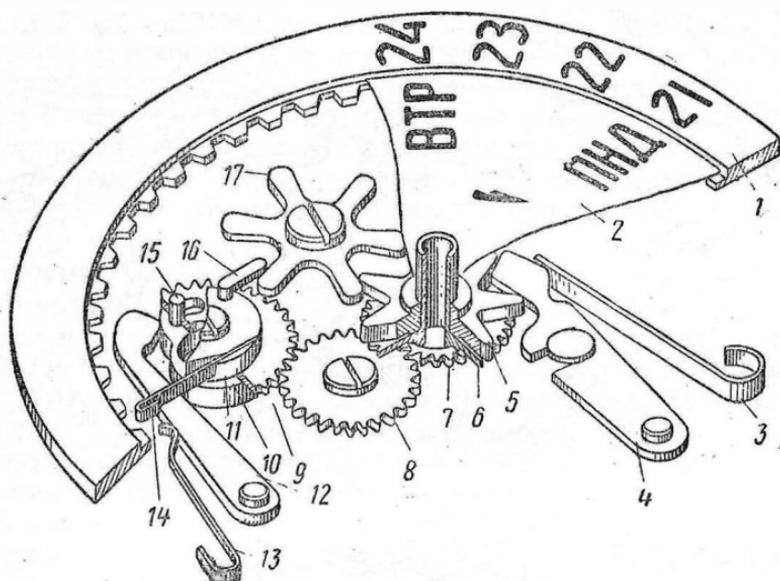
Кинематическая схема двойного календарного устройства мгновенного действия:
